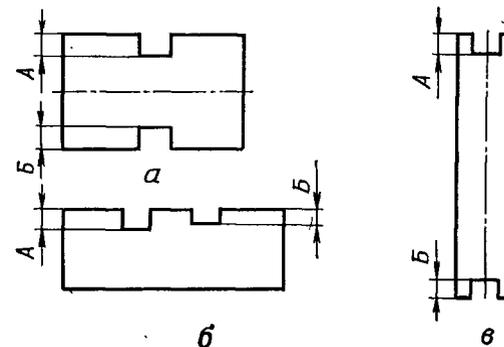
Калибры и шаблоны для проверки выхода бойка:
